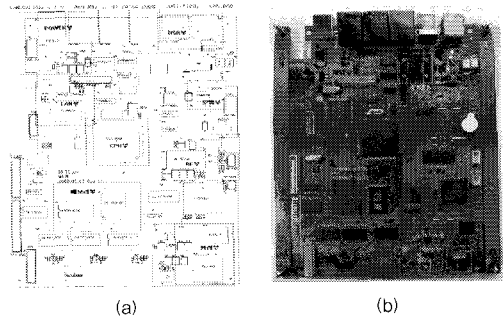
단말기 설계. (a) PCB 레이아웃, (b)메인 보드
